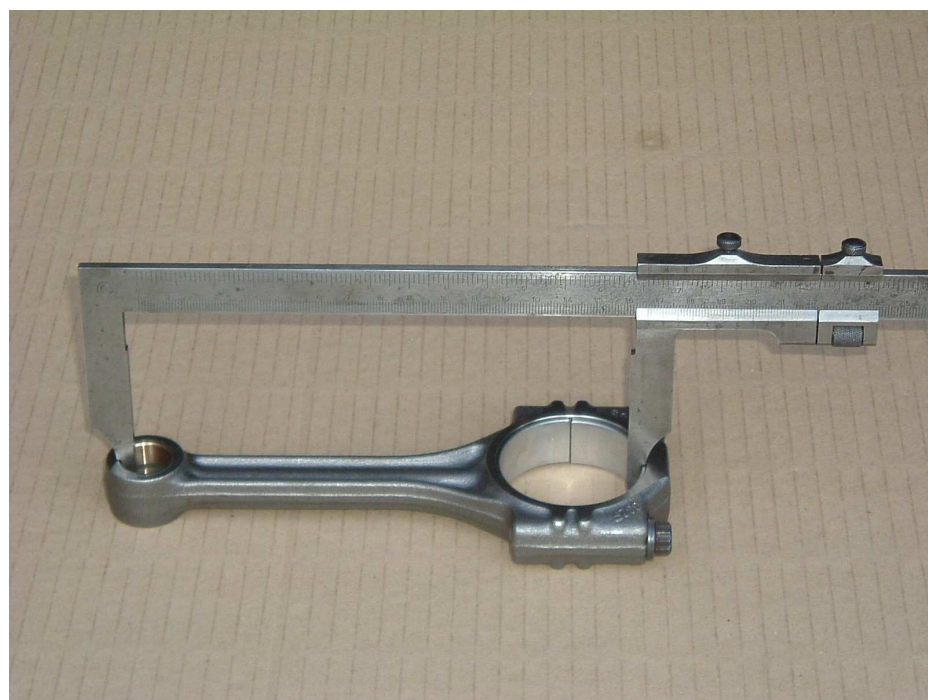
e. Měření šířky ojnicí pánve ložiska
